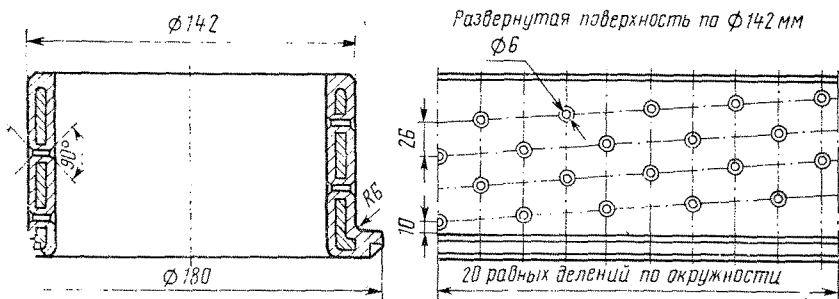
Разрез и развертка плавающей втулки паровоза Л
